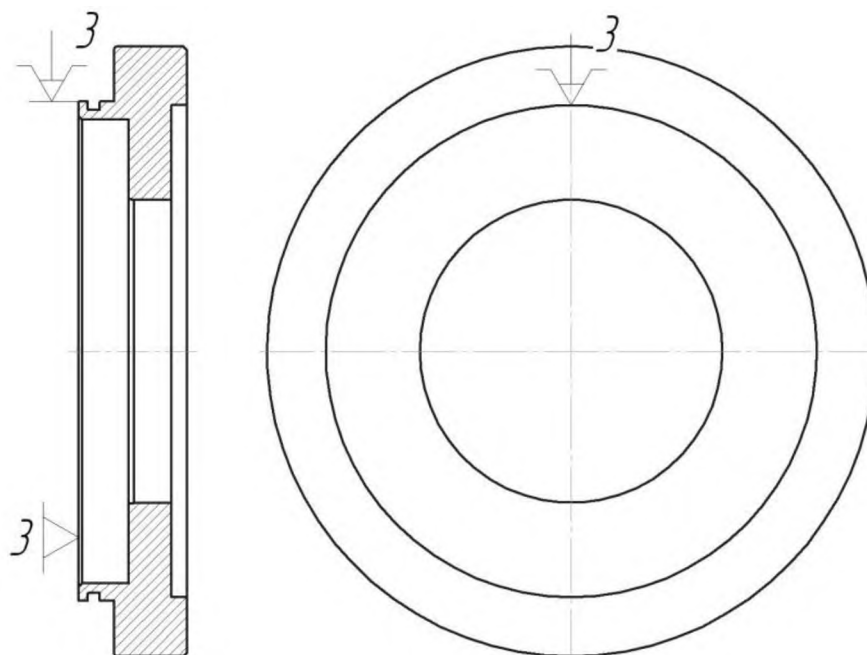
Схема базування на токарному верстаті (Установ Б)
